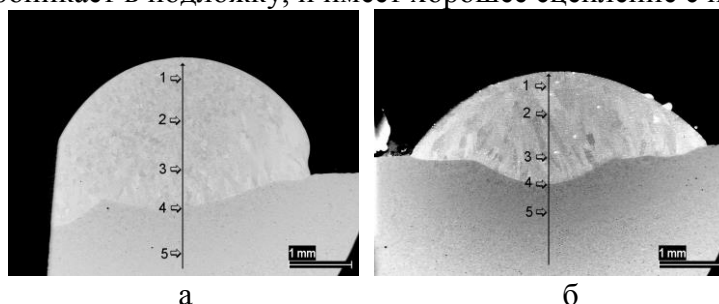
Микрошлифы дорожек лазерной наплавки стандартного порошка на основе никеля 1350 (а) и с добавками нанокарбида тантала (б).
